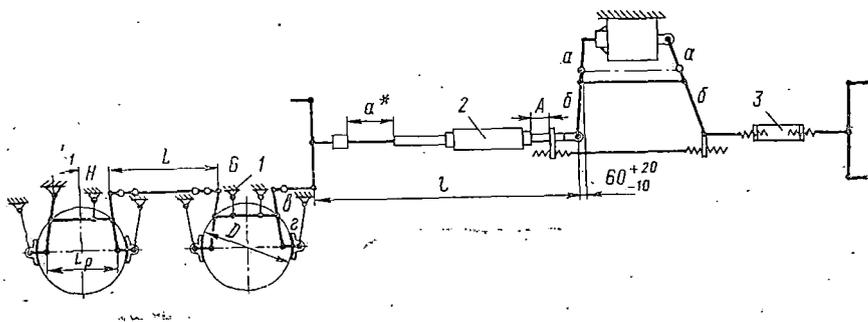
Схема установочных размеров при регулировке рычажной передачи пассажирского вагона
